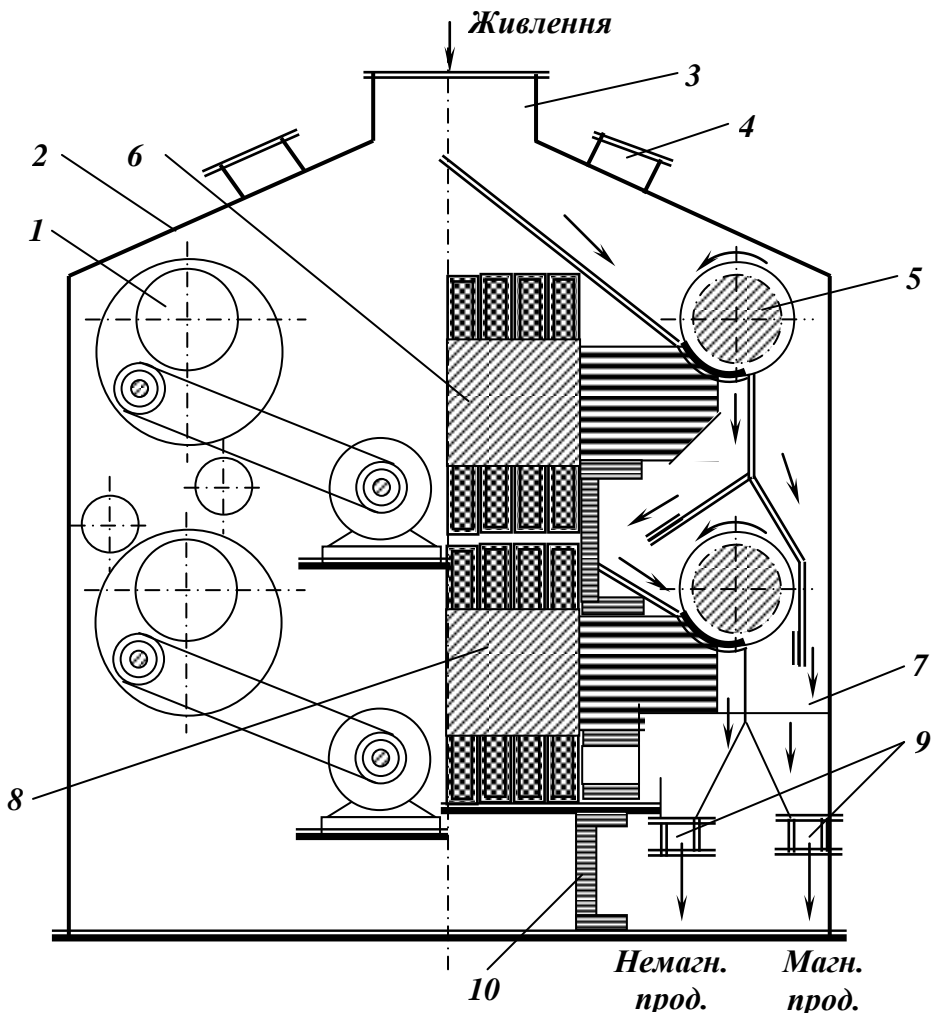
Схема електромагнітного валкового сепаратора типу 8ЕВС-16/100. 1 – привод; 2 – корпус; 3 – живильник; 4 – аспіраційний патрубок; 5 – валки; 6 – верхня електромагнітна система; 7 – ванни; 8 – нижня електромагнітна система; 9 – розвантажувальні пристрої; 10 – рама.
